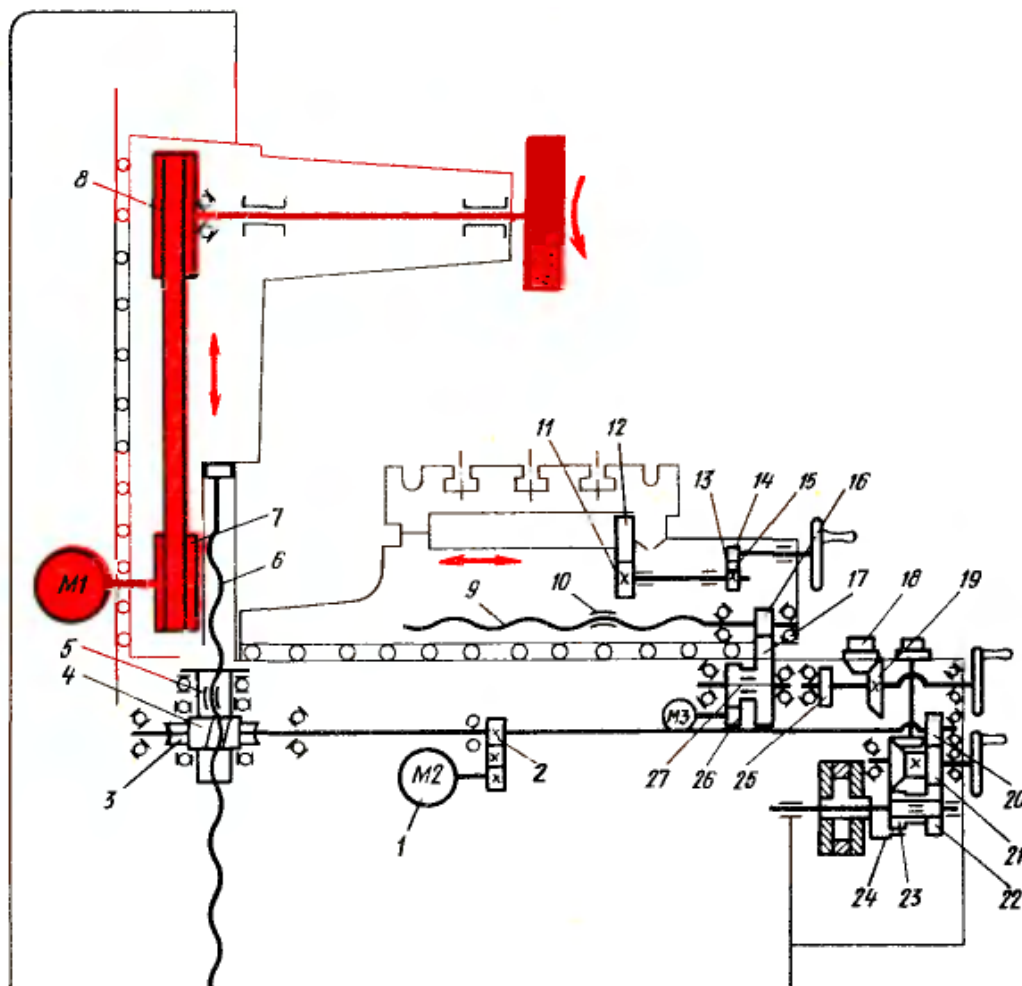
Кинематическая схема плоскошлифовального станка с горизонтальным шпинделем
